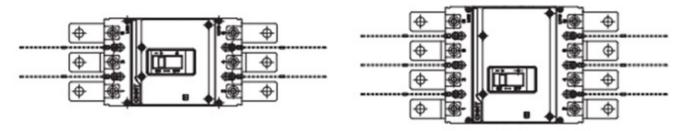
Схема установки соединительной пластины NXM(S)-63, 125, 160, 250
